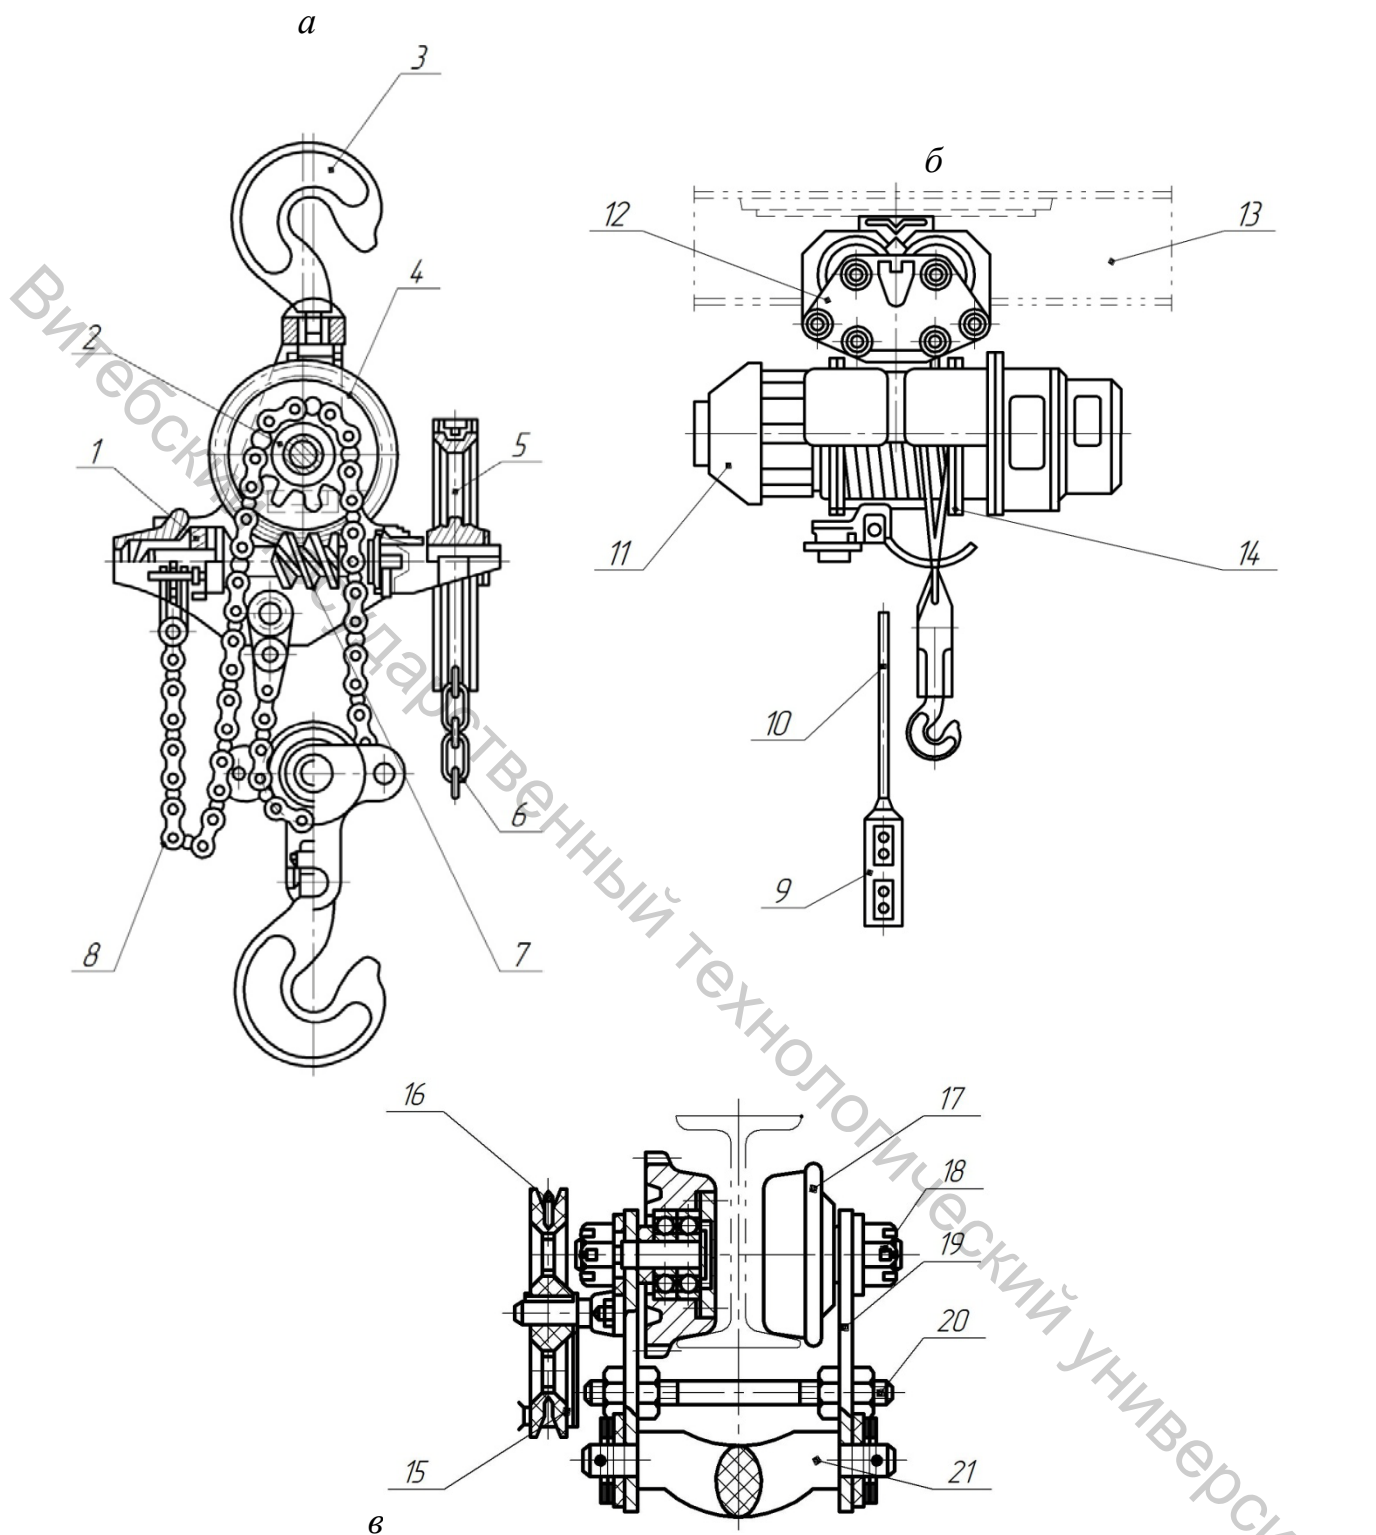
Таль (а), тельфер (б) и монорельсовая тележка (в) с ручным механизмом передвижения для подвешивания тали и тельфера: 1 – тормоз; 2 – звездочка; 3 – крюк; 4 – червячное колесо; 5, 15 – приводные колеса; 6 – приводная цепь; 7 – червяк; 8, 16 – грузовые пластинчатые цепи; 9 – пульт управления; 10 – гибкий кабель; 11 – электрический двигатель; 12 – тельфер; 13 – монорельсовый путь; 14 – канатный барабан; 17 – колесо; 18 – ось; 19 – боковая накладка; 20 – шпилька; 21 – траверса
